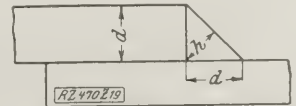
Querschnitt einer Kehlschweißung.
